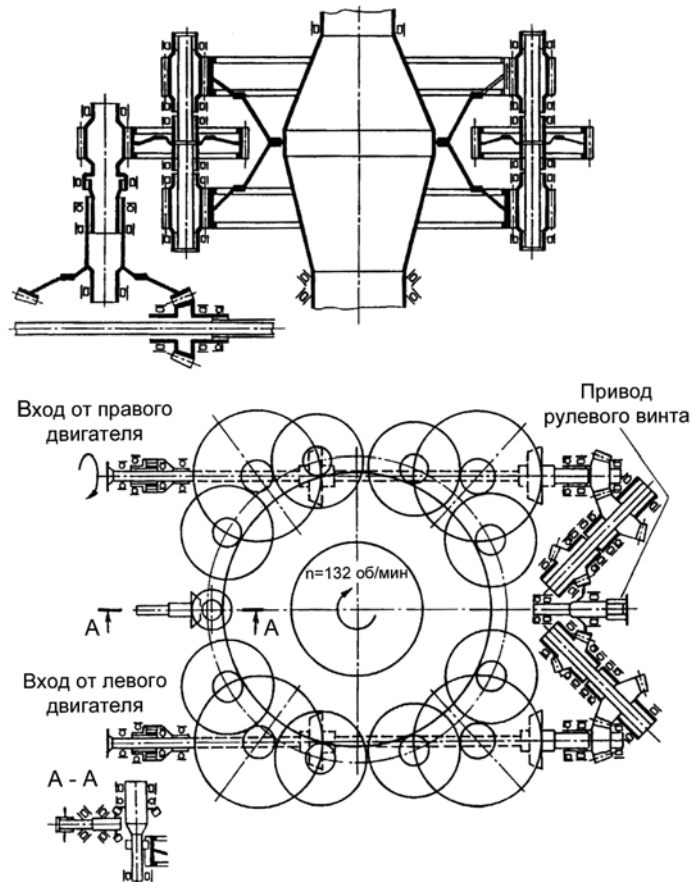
Кинематическая схема главного редуктора вертолета Ми-26
